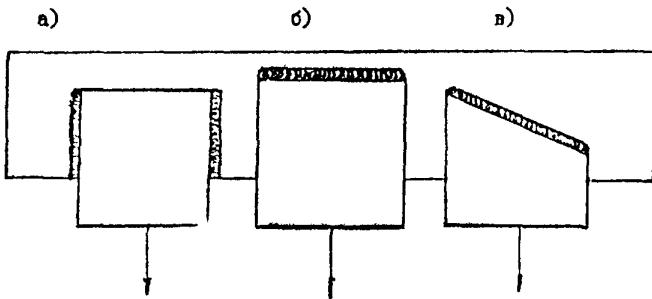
Положение сварных швов относительно действующего усилия:
